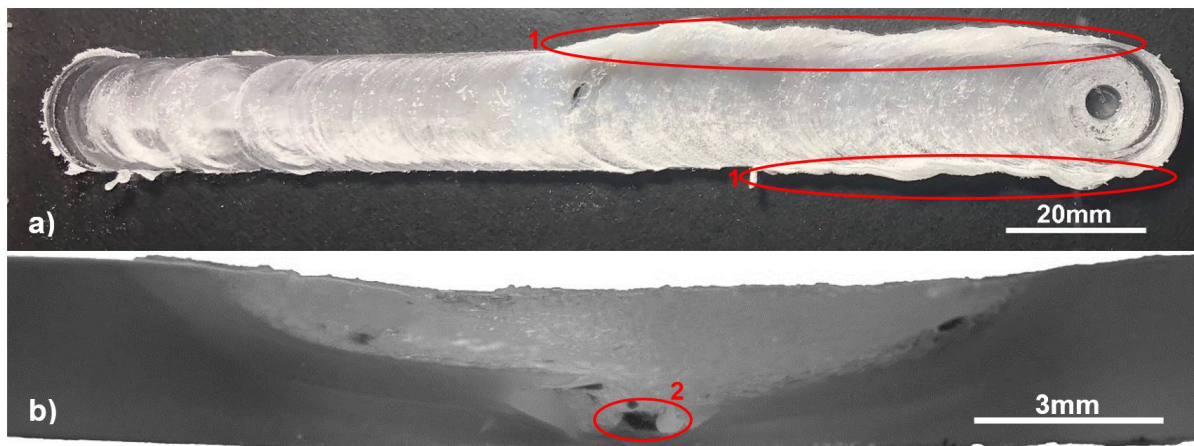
Defeitos comuns na soldagem por *Friction Stir Welding* 1:Flash Defect e 2:Tunnel Defect, ambos encontrados em chapas soldadas de policarbonato, sendo (a) superfície soldada e (b) seção transversal [Autor].
